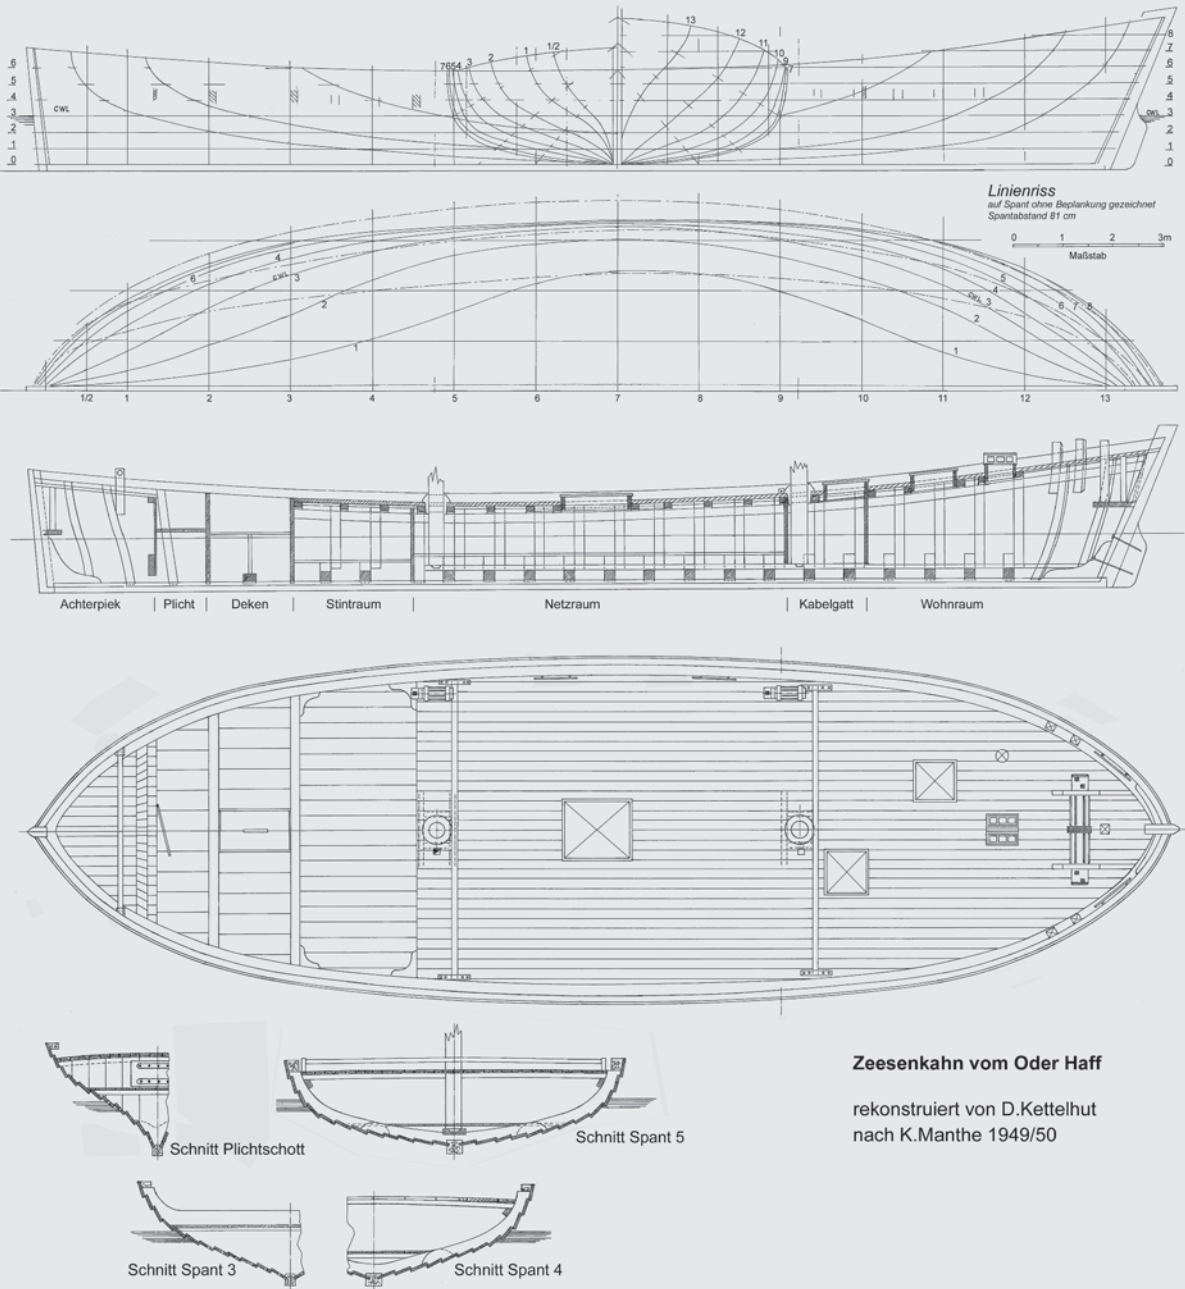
Zeesenkahn vom Stettiner Haff: Linierriss, Längsschnitt, Decksplan und Konstruktions-
